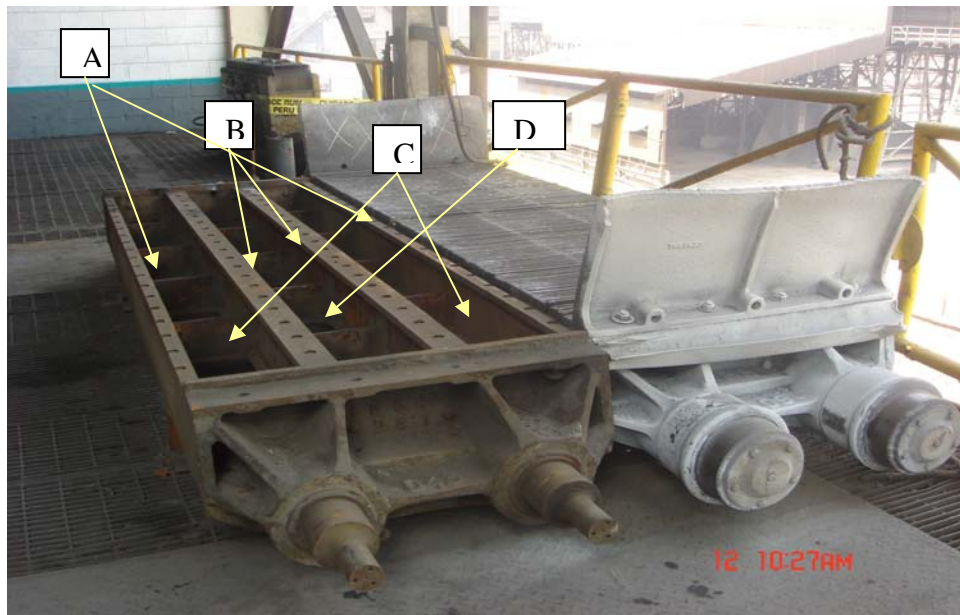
A: Desmontaje del carro sinter para inspección de su linealidad.
